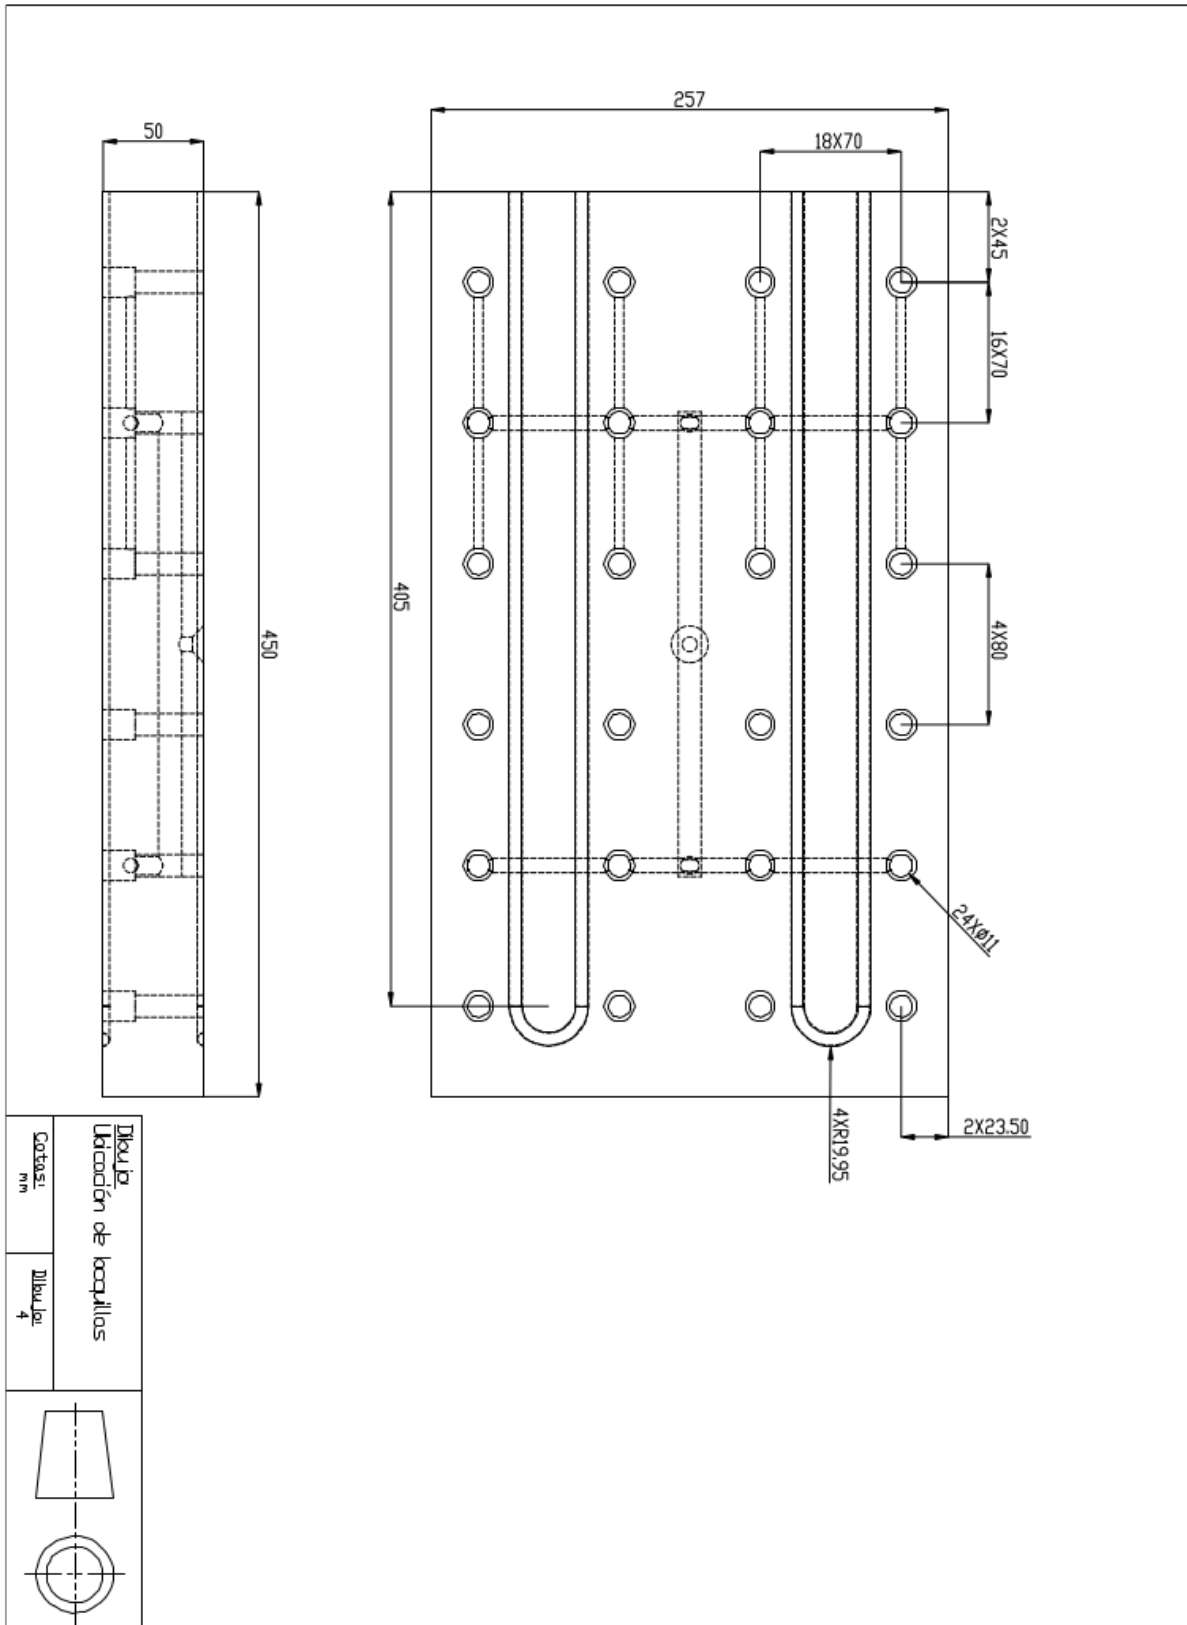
Dimensión y ubicación de barrenos para boquillas
